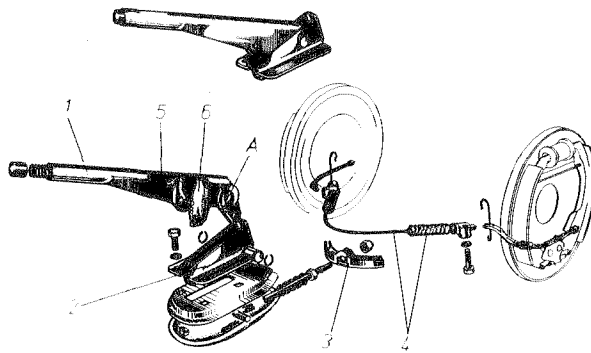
B Despiece de un mecanismo de freno de mano.
